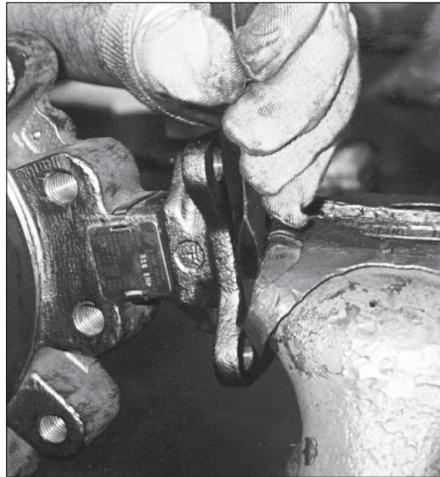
Снятие верхнего вала с верхней ступицы диска.
